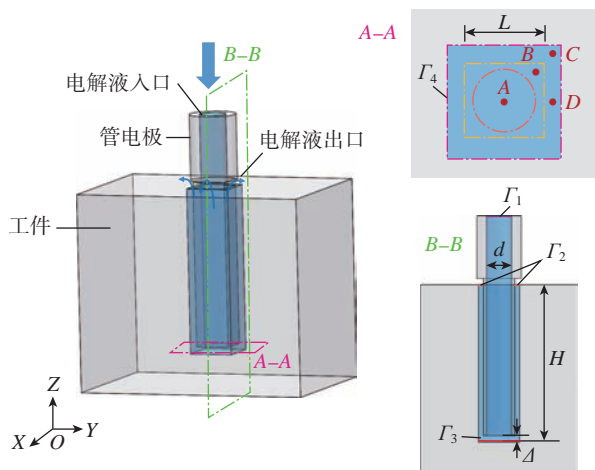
工件振动辅助管电极电解加工方孔仿真模型示意图
